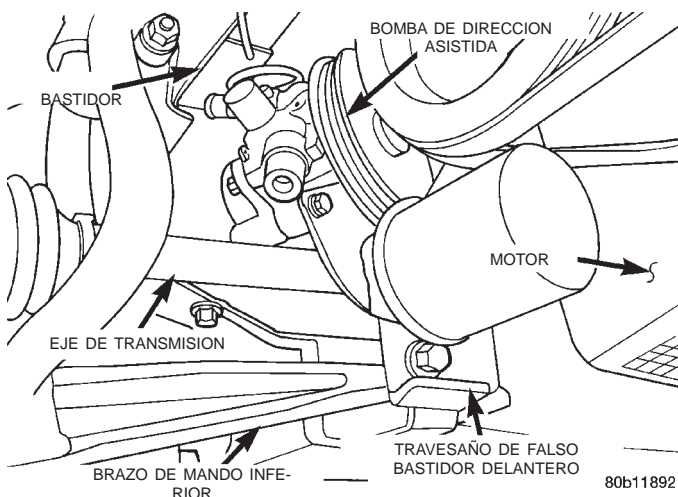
Soporte de montaje de la bomba de dirección asistida
